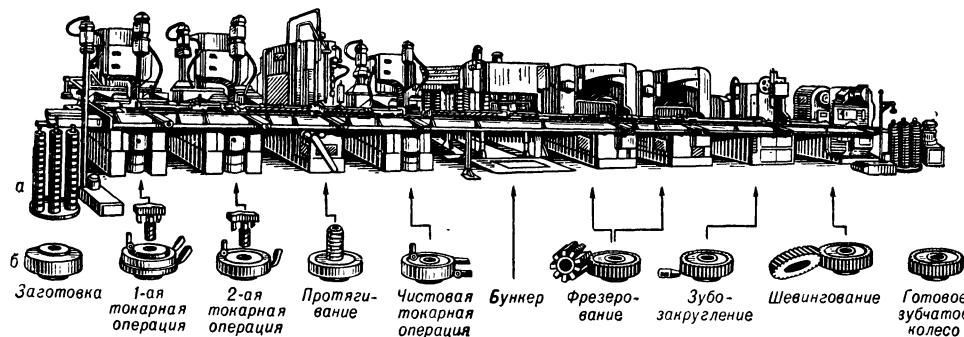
Типовая автоматич. линия для обработки цилиндрич. зубчатых колес: а — общий вид линии; б — технологич. процесс, осуществляемый на линии.
